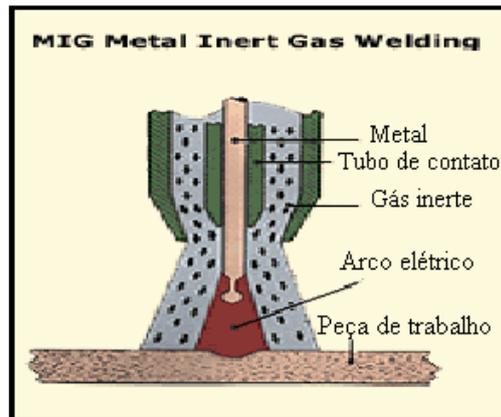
Processo de soldagem *Metal Inert Gas* – MIG.
